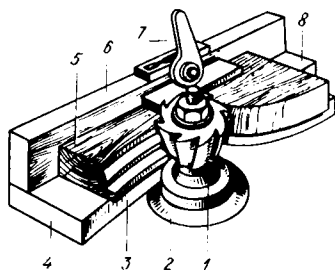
Обработка криволинейной кромки на фрезерном станке:
